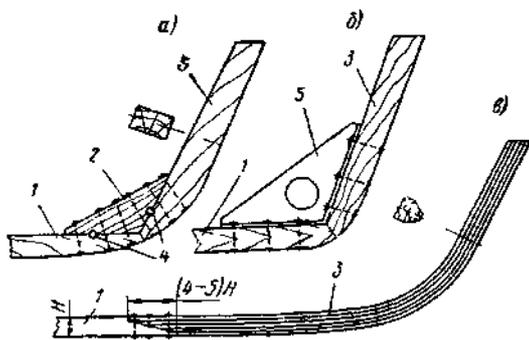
Форштевни: а — с деревянным кнопом; б — с металлическим кнопом; в — гнукклееный.
